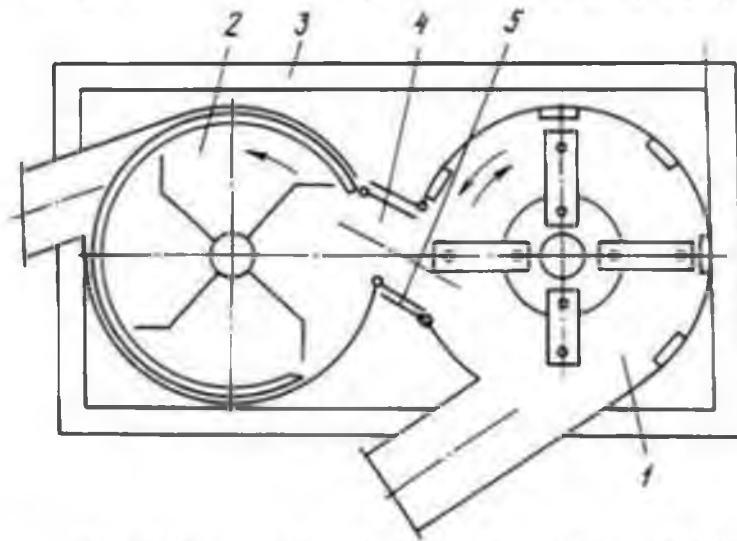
Дробарка з двома робочими органами: 1 – молоткова дробарка; 2 – ріжуча машина; 3 – рама; 4 – з'єднувальний канал; 5 – стінки каналу
